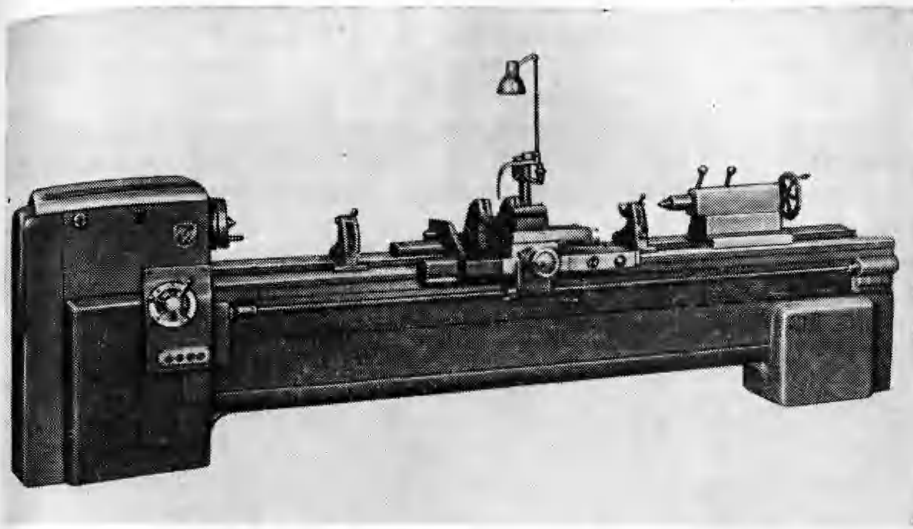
Универсальный токарно-копировальный полуавтомат мод. 1732.
